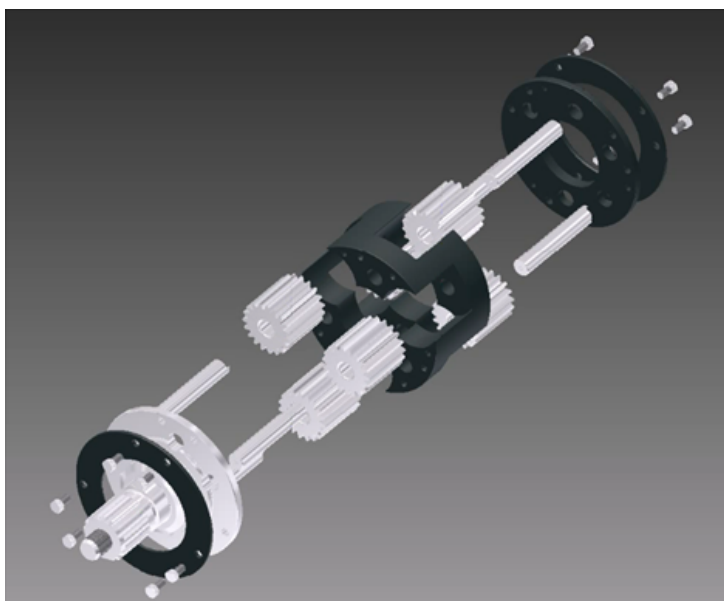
Планетарний механізм К2 із щепленими сателітами- збірка,рознесений вигляд.
